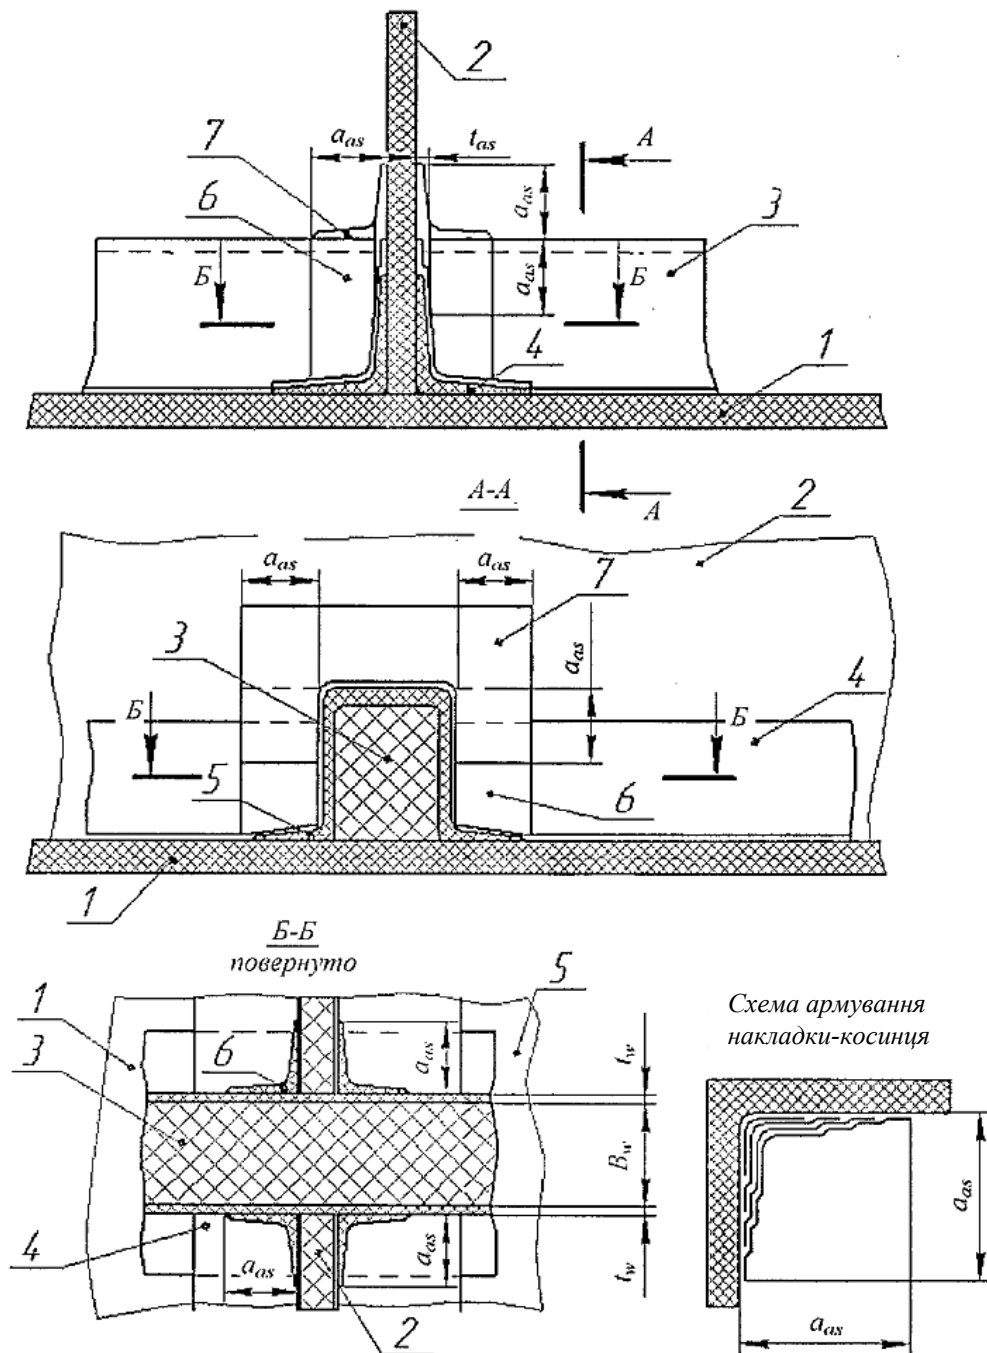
Вузол проходу поздовжньої балки набору П-подібного профілю через водонепроникну поперечну перегородку:
